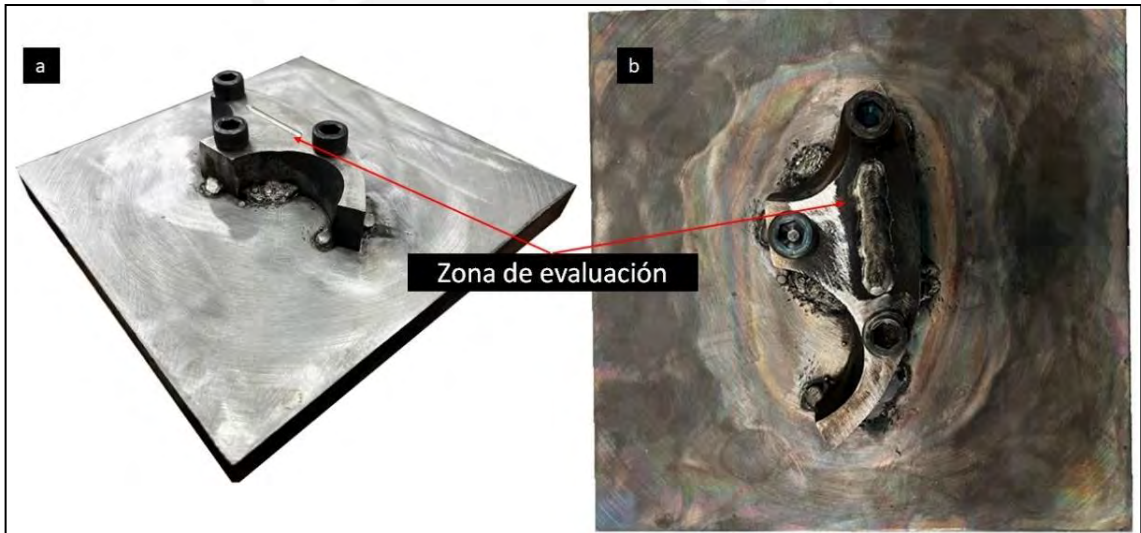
Montaje de ensayo EE de la culata, (a) antes del cordón de soldadura en la zona de evaluación, (b) luego del cordón de soldadura en la zona de evaluación.
